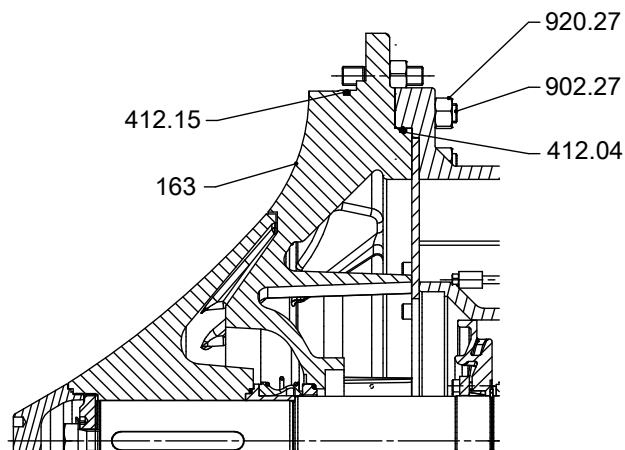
Besonderheit Hydraulik - Pumpenaggregat mit Kühlsystem
